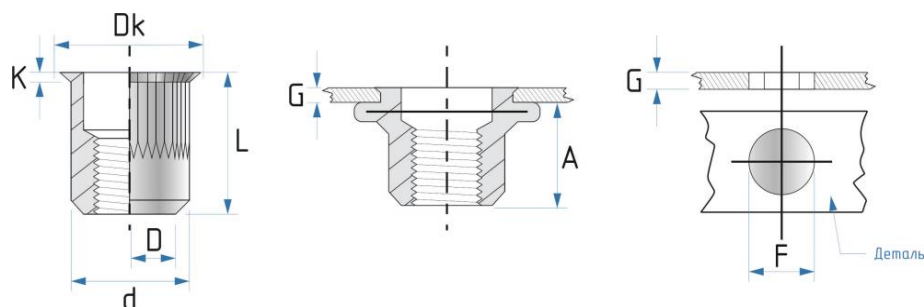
Заклёпка резьбовая цилиндрическая с насечками,
